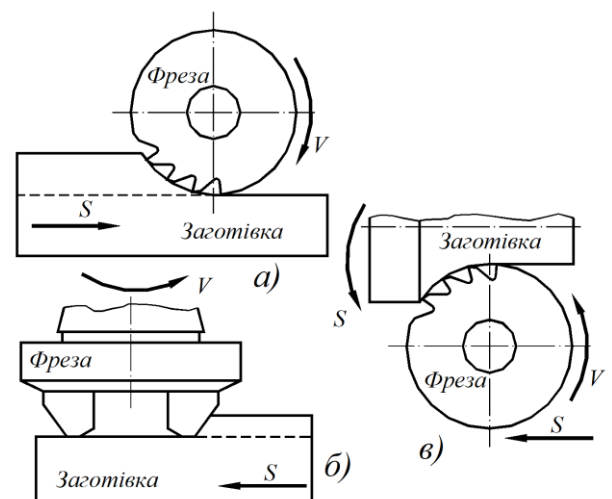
Види фрезерування: а) циліндричне; б) торцеве; в) кругове.
